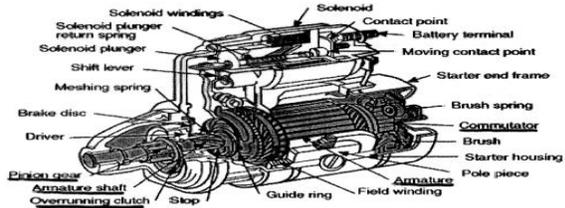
Esquema 1 de um motor de arranque moderno com os elementos rotativos a sombreado.
